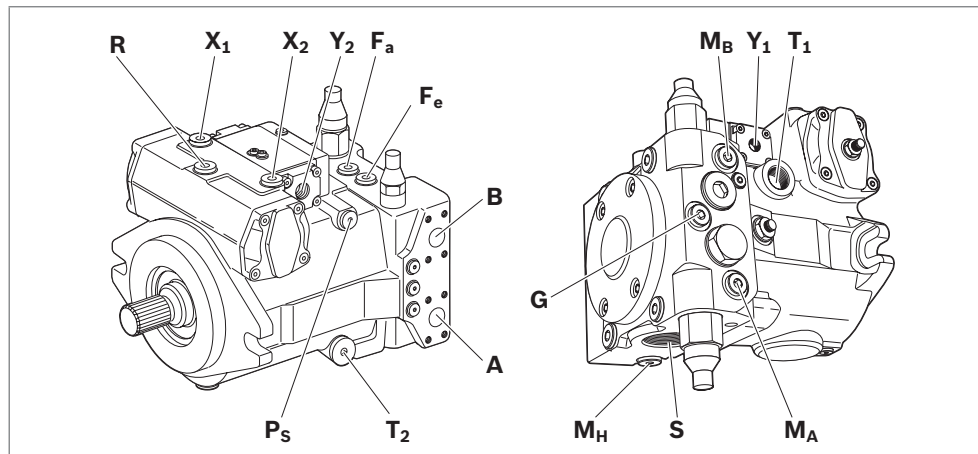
Обзор присоединений A4VG, номинальный размер 28
